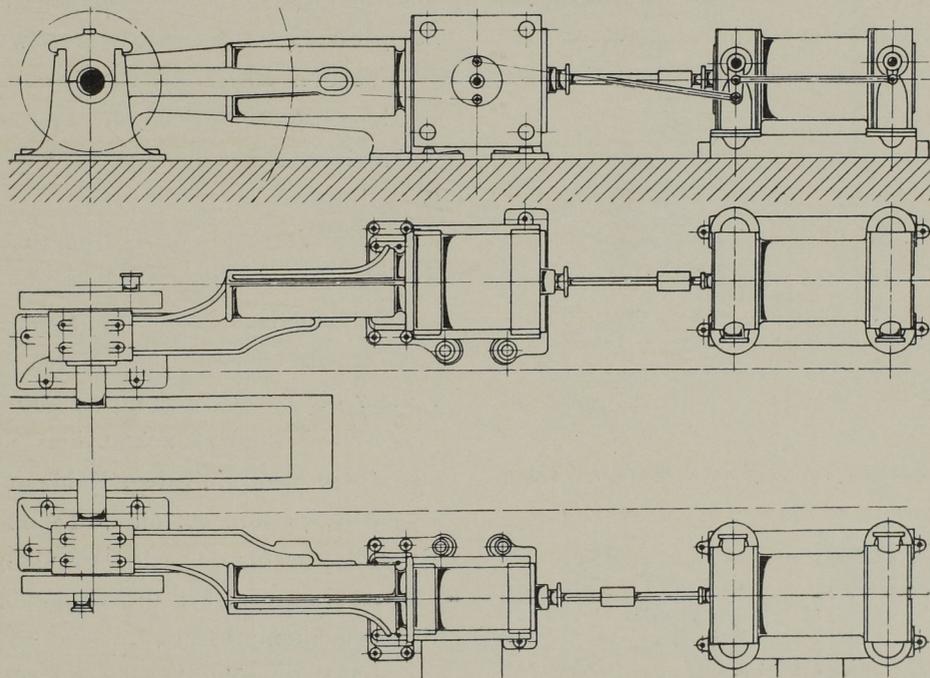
Seitenansicht und Grundriss. Masst. 1:64.
